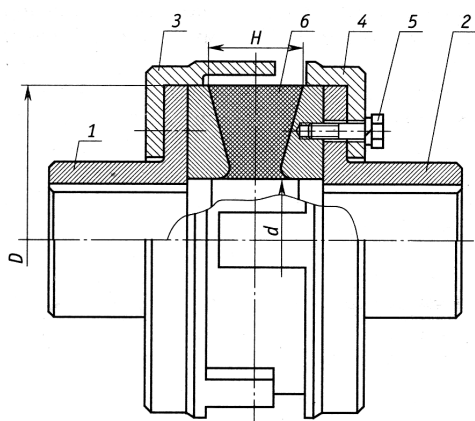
Муфта с резиновой конической шайбой: 1, 2 – полумуфты; 3, 4 – защитный кожух; 5 – винт; 6 – упругий элемент
